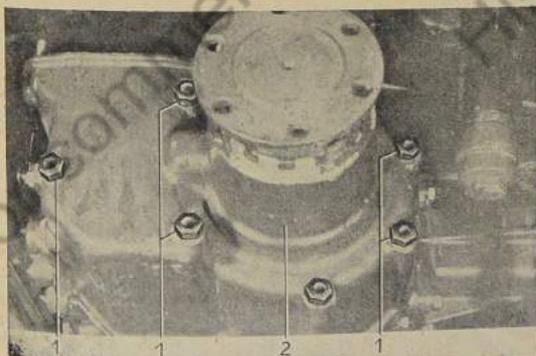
Gehäuse für Freilaufsperr (Schaltgehäuse) am Getriebe abschrauben
